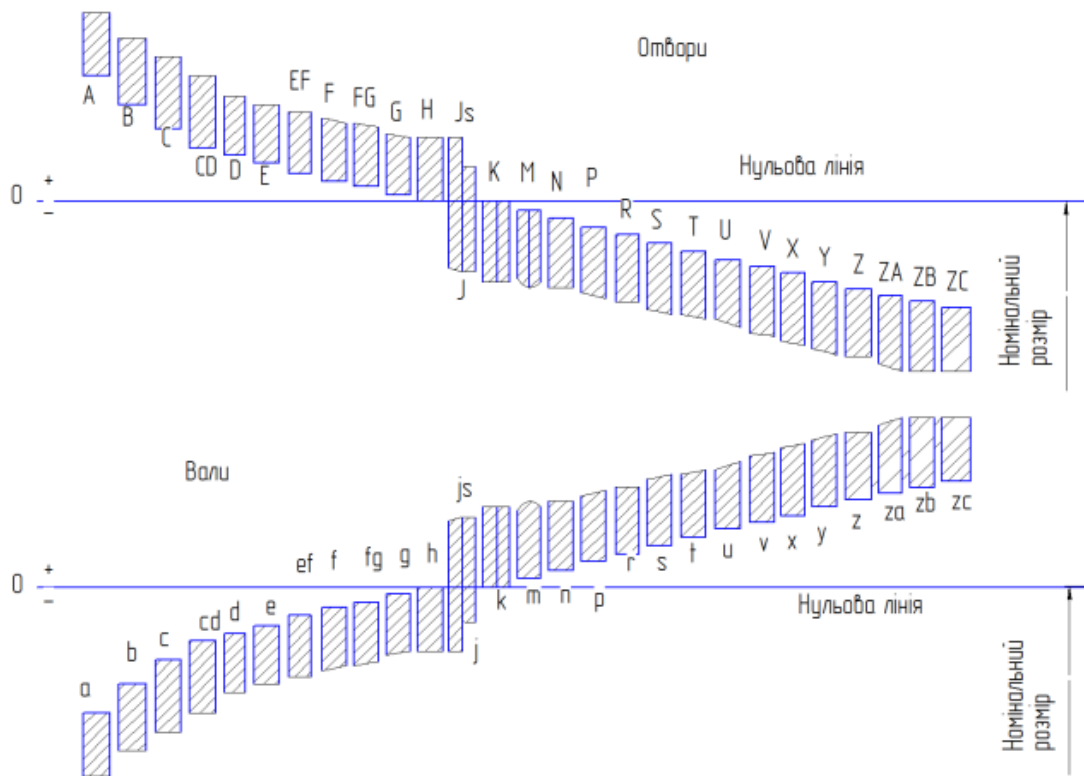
Схема розташування полів допусків з різними основними відхилами
